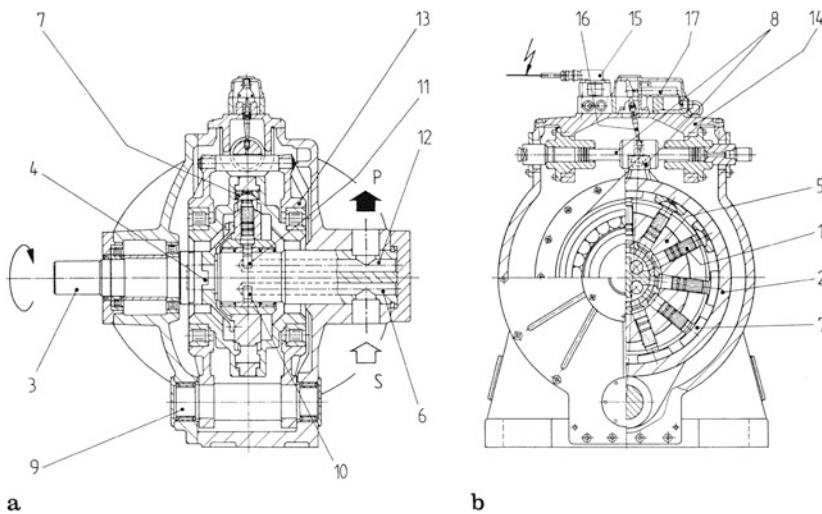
Radialkolbenpumpe, innen beaufschlagt (RX, Wepuko Hydraulik) mit elektrohydraulischer Stelleinrichtung (Nr. 6) als Baustein eines Verstellprogramms für die Pumpensteuerung. a Längsschnitt in Schwenkchse; b Querschnitt senkrecht zur Schwenkchse
